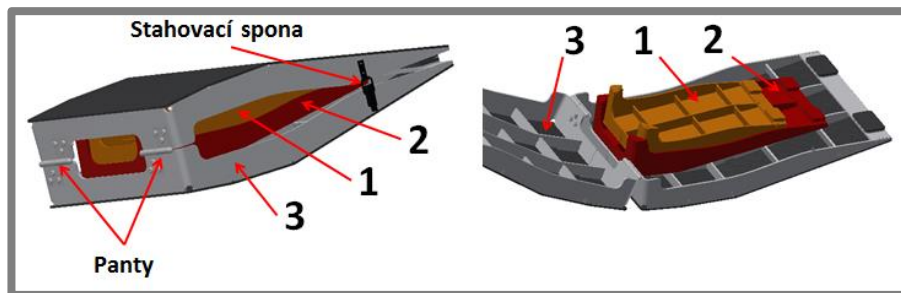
Umístění jednotlivých nájezdových ramp
